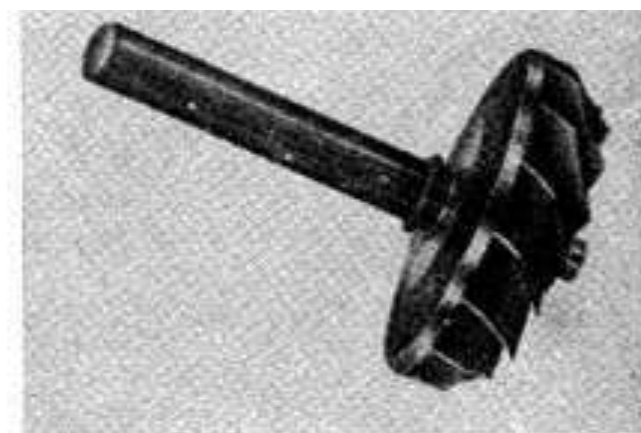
Ротор турбоагрегата. Сварка трением. Колесо из жаропрочной аустенитной стали, вал — из перлитной стали. Диаметр в месте сварки 20 мм.
